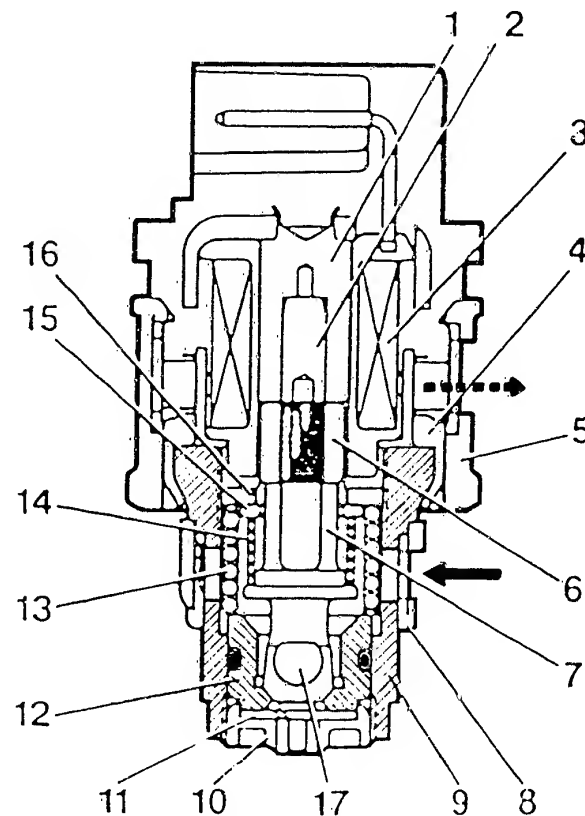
Schnitt durch das elektromagnetische Einspritzventil mit seinen Einzelteilen: 1 Magnetpol – 2 Hubzylinder – 3 Magnetspule – 4 dito Gehäuse – 5 Dampfblasenfilter – 6 Ankerring – 7 Anker – 8 Treibstoff-Einlassfilter – 9 Ventilgehäuse – 10 Strahlzerstäuber – 11 Zerstäuberscheibe – 12 Ventilsitz – 13 dito Feder – 14 Ventilankerfeder – 15 Führungsring – 16 Einstellschraube (fest eingestellt) – 17 Ventilkolben.
